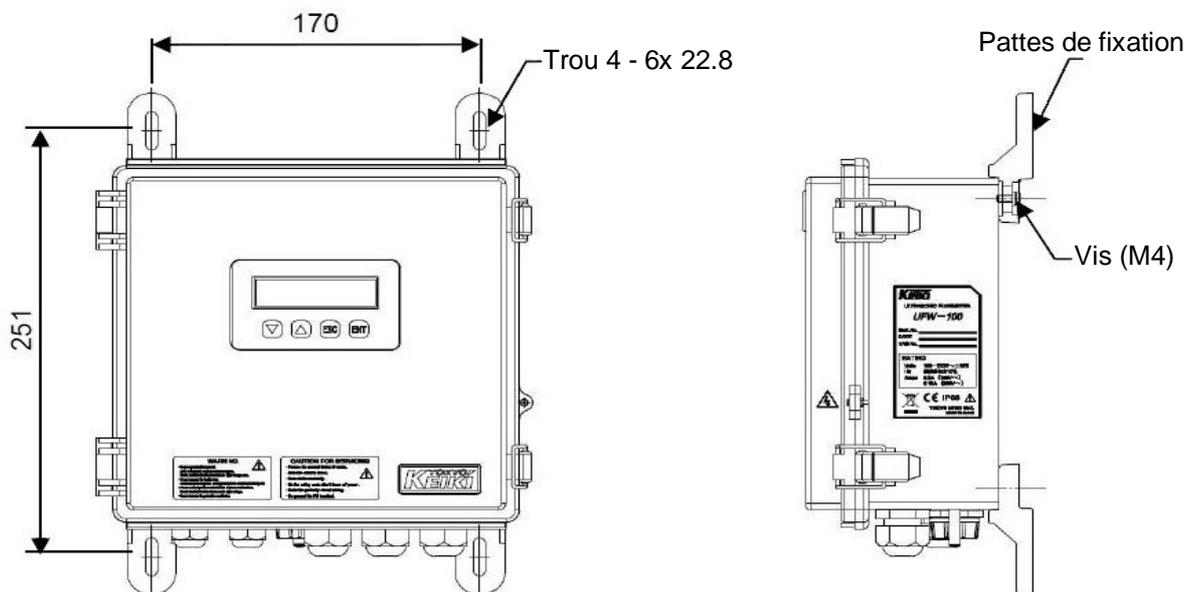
Fixation contre le mur (pattes de fixation, accessoires normaux)
